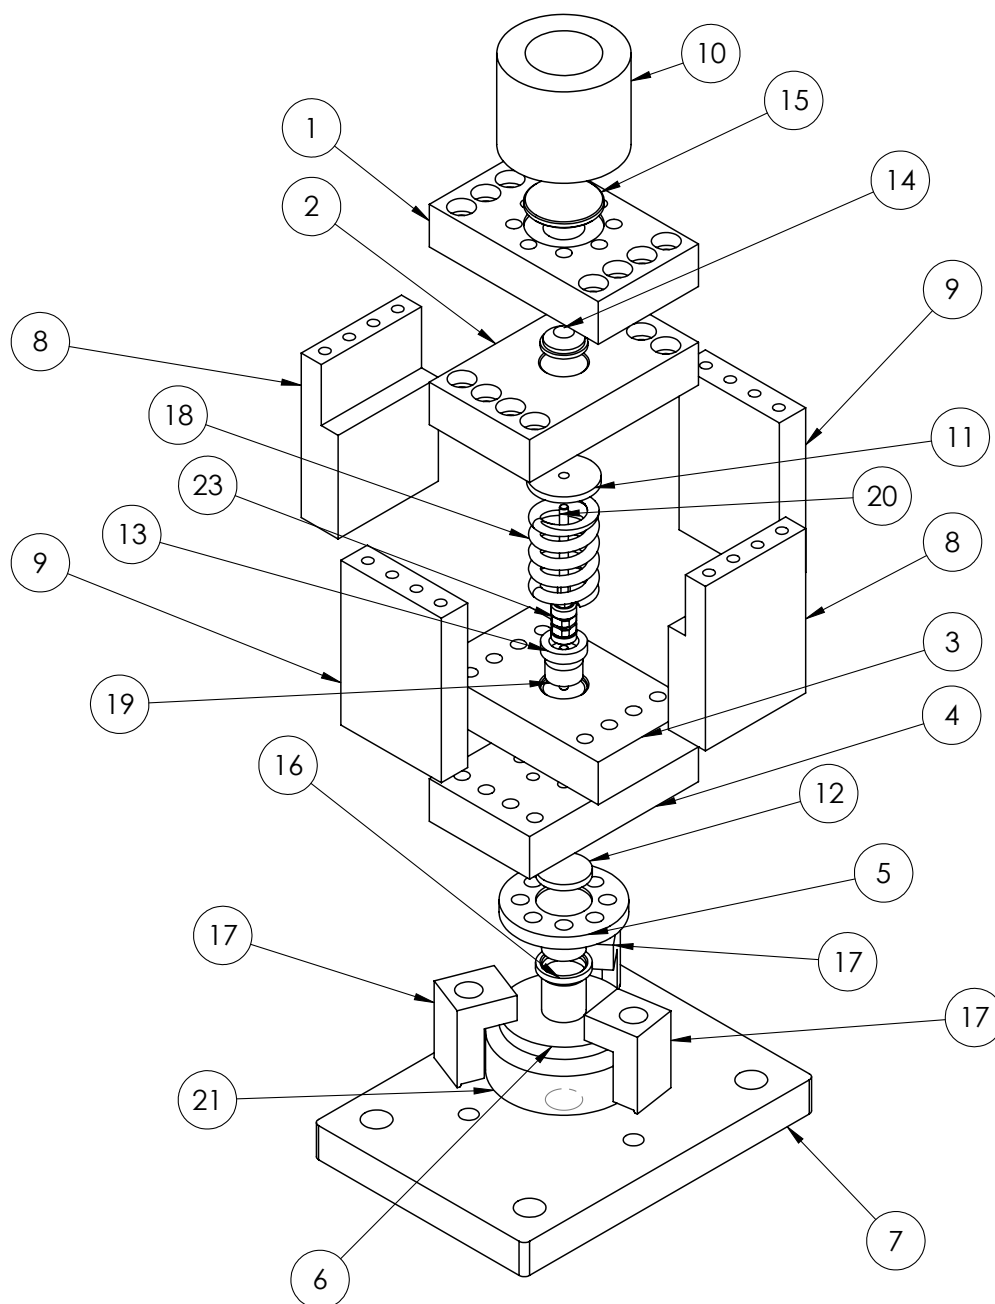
Vue éclatée du dispositif expérimental.
